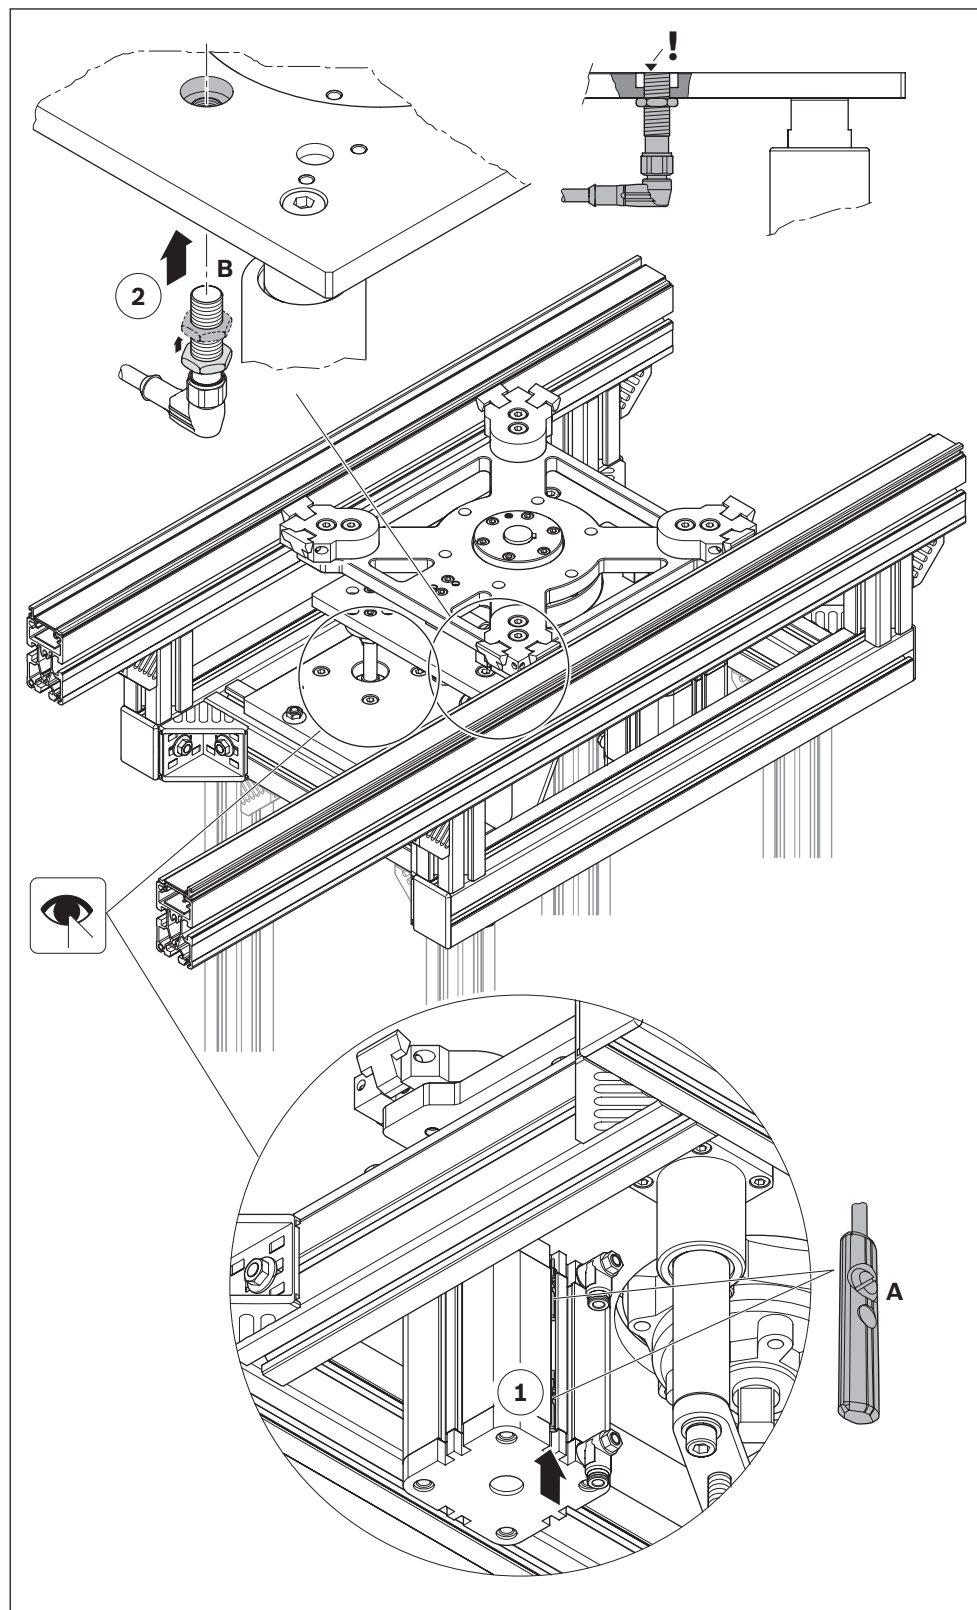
Montaje de la detección de posición para elevación vertical y rotación horizontal (aquí tamaño constructivo 2 180° para WT 2, WT 2/F)
